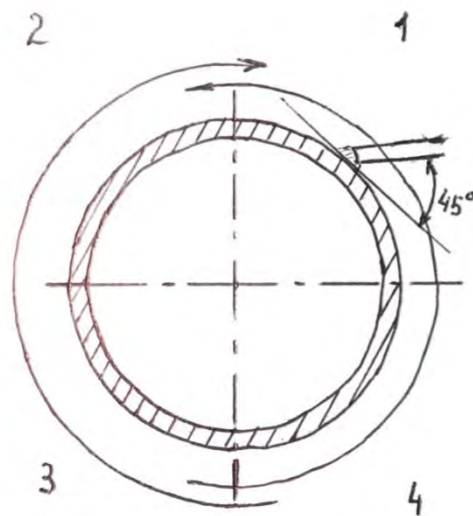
Последовательность сварки кольцевого шва трубы
